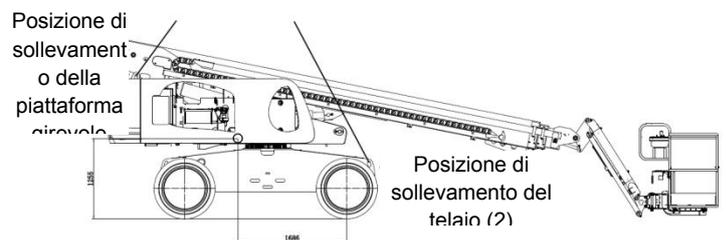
Schema di collegamento durante il sollevamento della macchina
